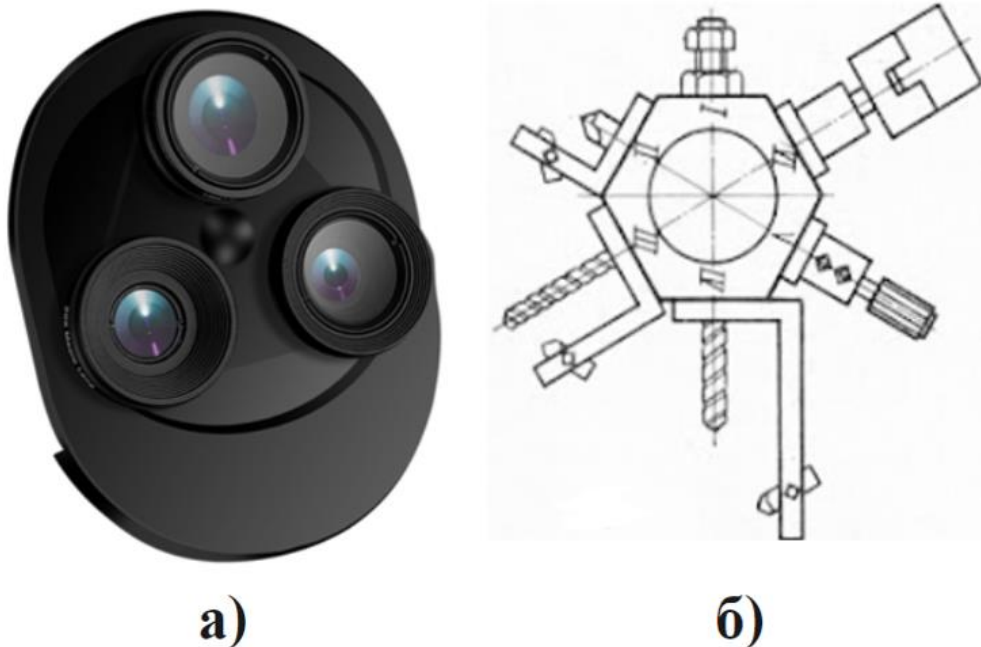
Механізми зміни РО (а – на камері смартфона[18] б – револьверний станок[19])
